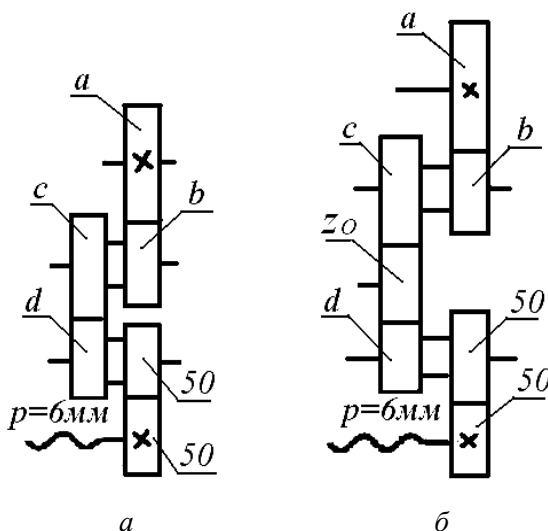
Схемы установки сменных зубчатых колес гитары для нарезания винтовой канавки
